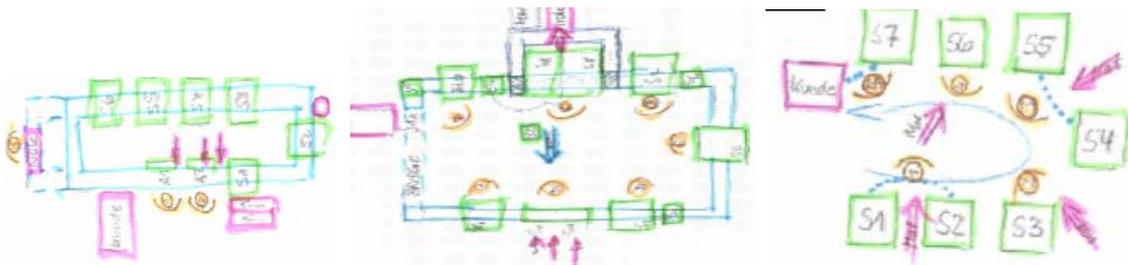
Skizzierung der möglichen Layouts für das Montagesystem
